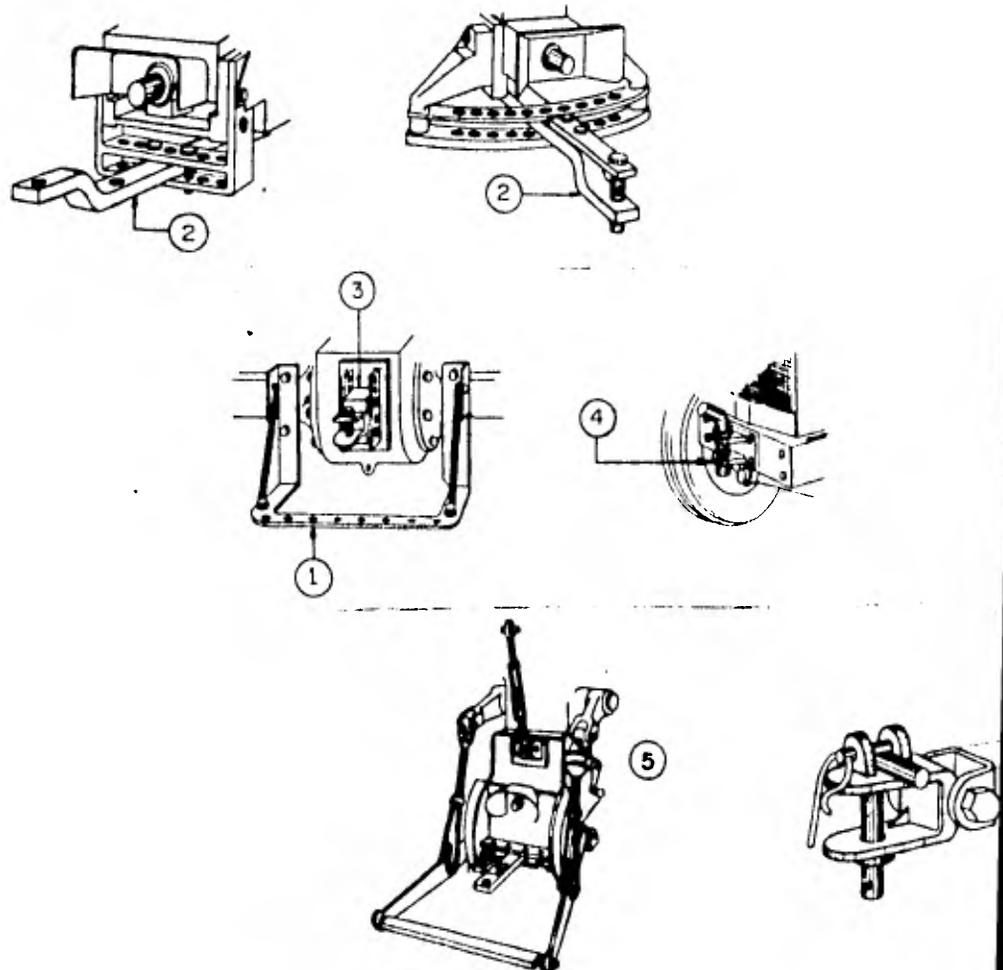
Barras de tiro y ganchos; 1, tipo standard. 2, oscilante. 3, gancho de tiro. 4, gancho de empuje. 5, enganche en tres puntos.
